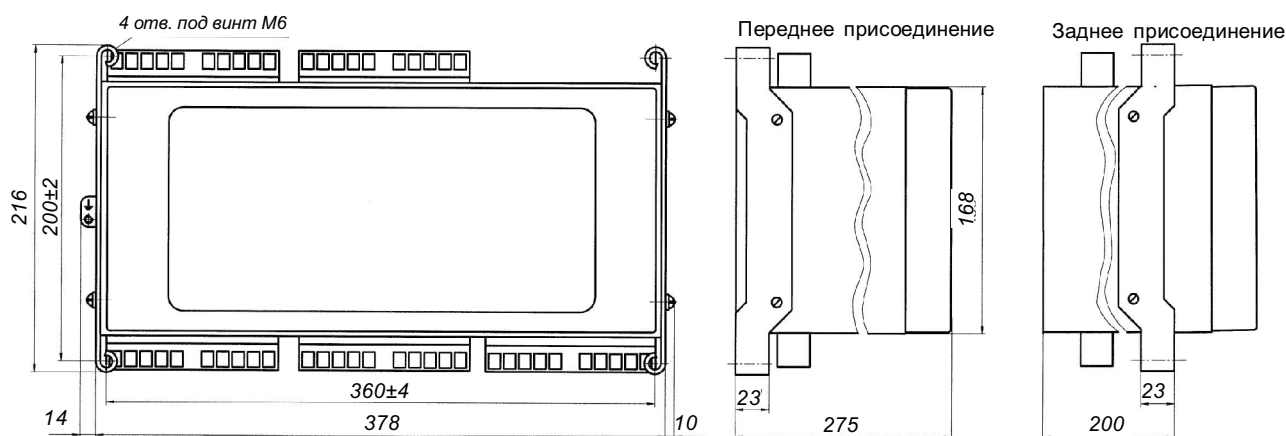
Габаритные, установочные размеры блока типа БЭ 2604
